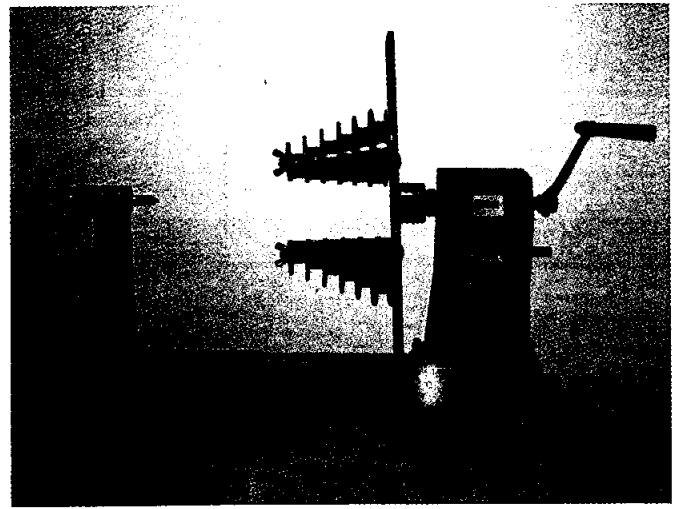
Bobinadora manual con molde de bobinas concéntricas.
